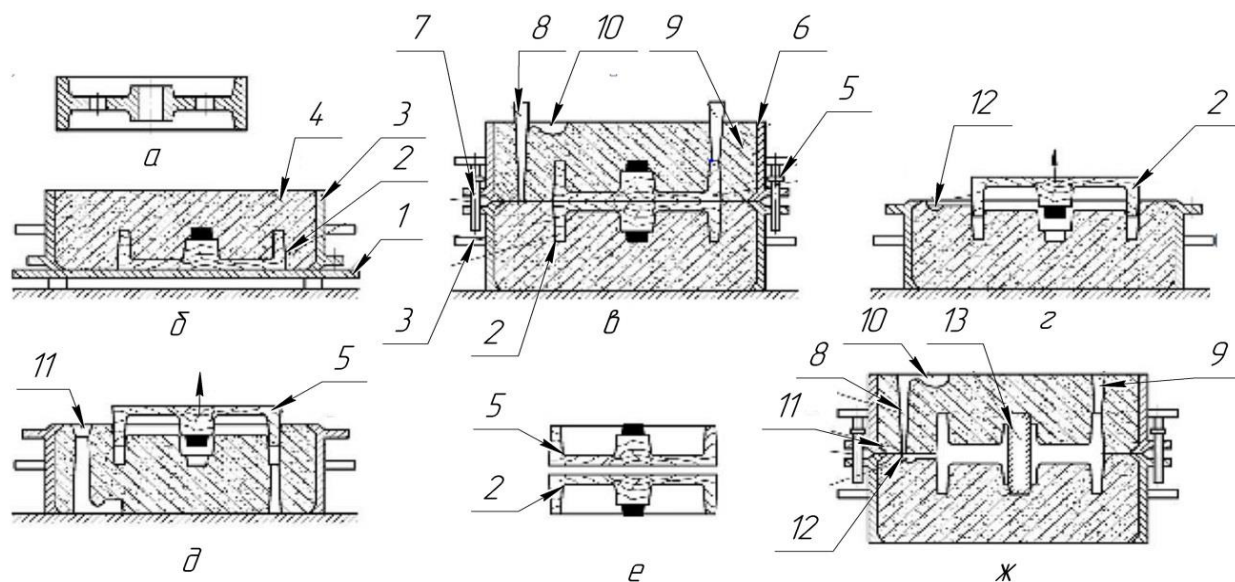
Форма для изготовления шкива, выполненная в двух опоках:
